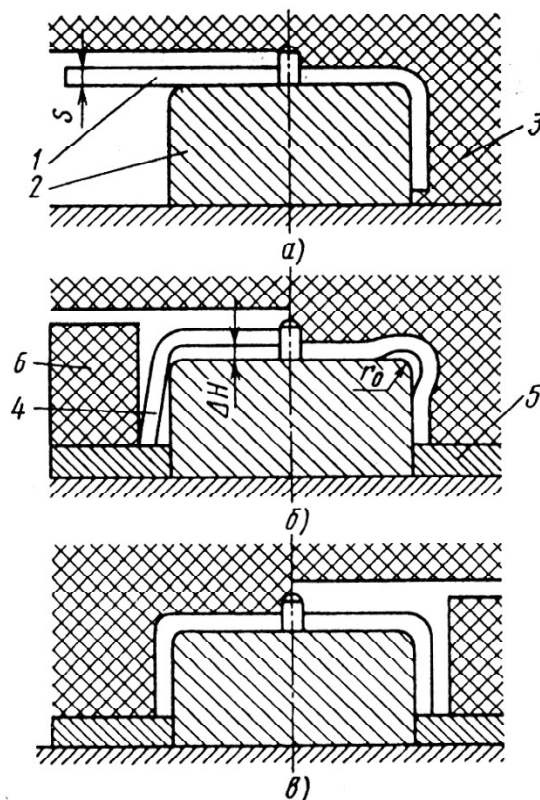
Схема устройства для стесненного изгиба эластичной средой с подпорами
